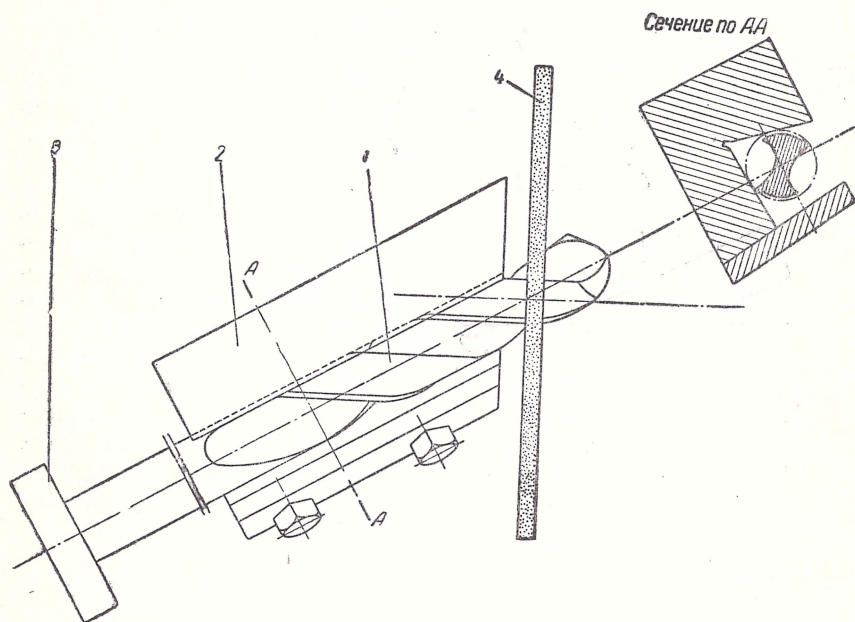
Приспособление для отрезки прибыли у заготовки сверла:
